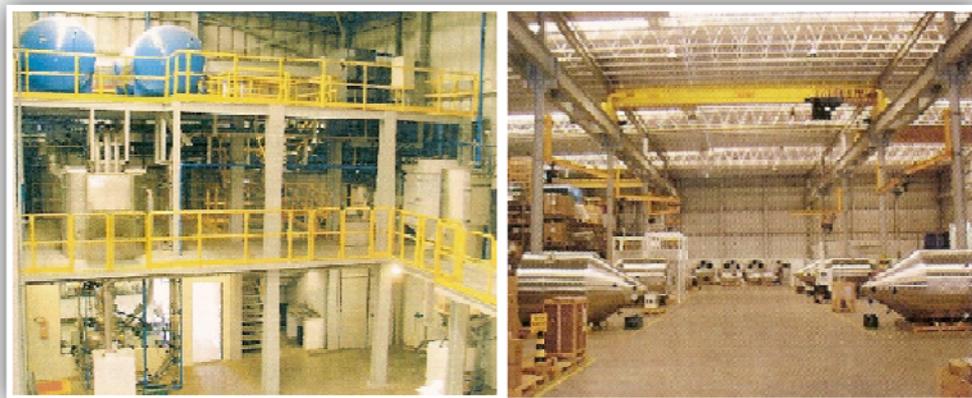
Planta Piloto e chão de fábrica, instalações da Dynamic Air do Brasil.
